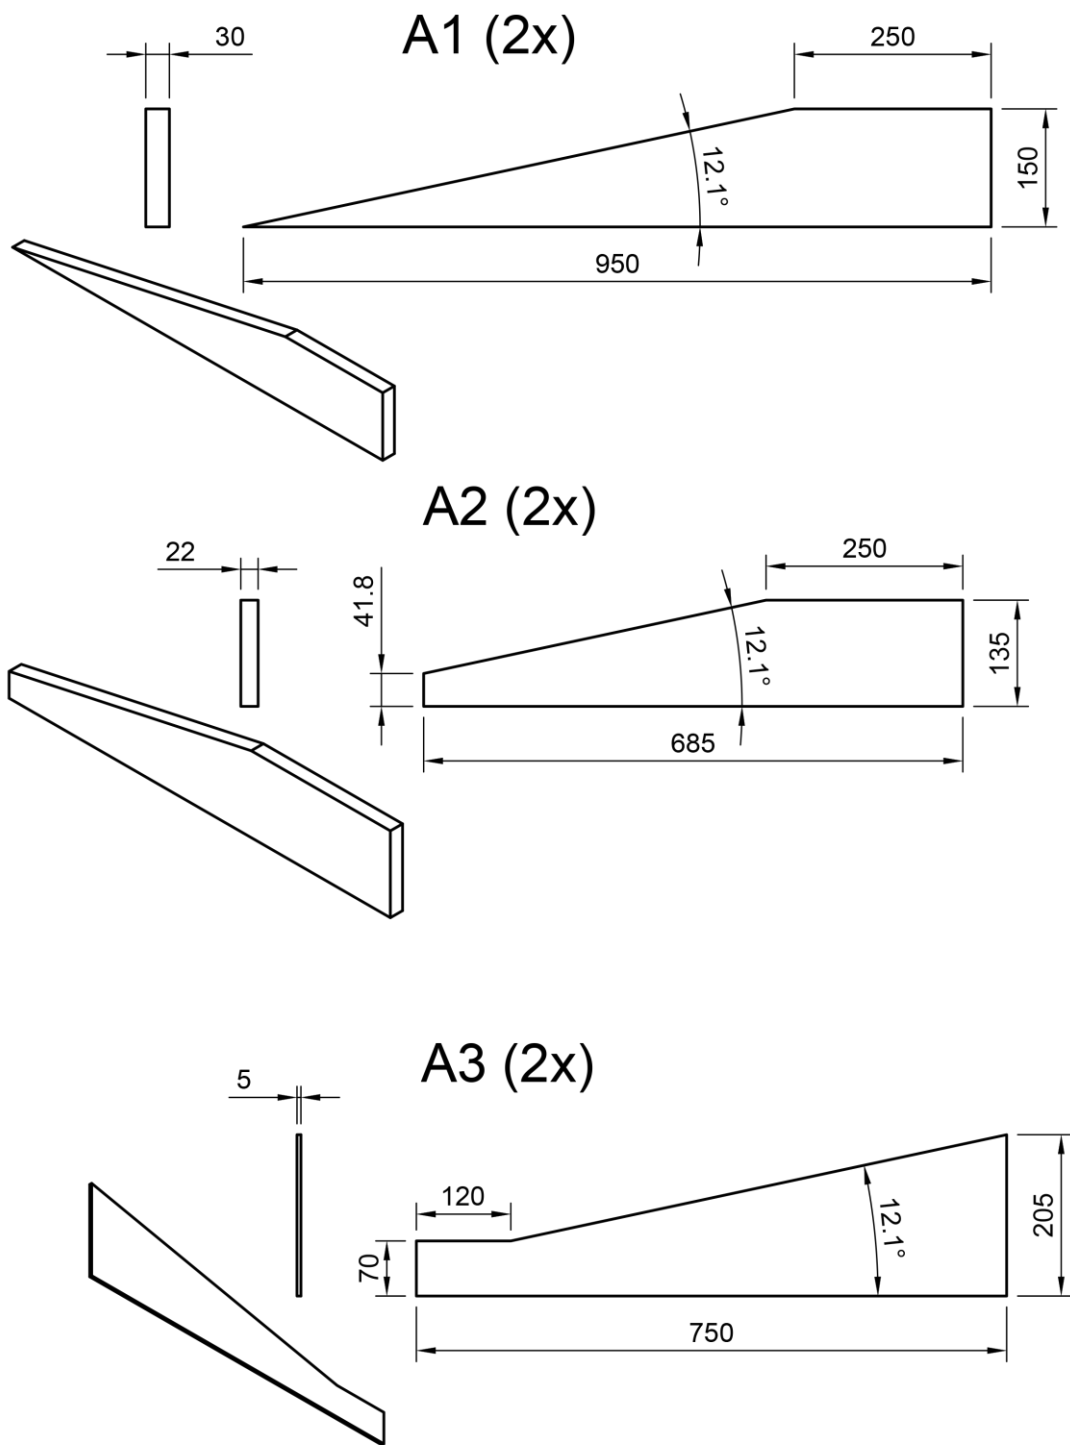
Ускоритель частиц – Детализированный вид - 2
